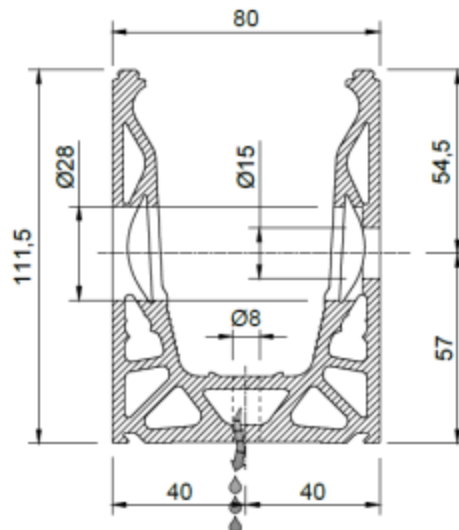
section transversale du profilé DF1012FR.60 avec indication de perçage pour drainage
